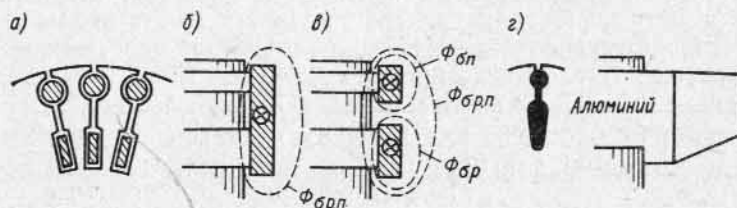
Форма исполнения обмоток ротора двухклеточного двигателя
